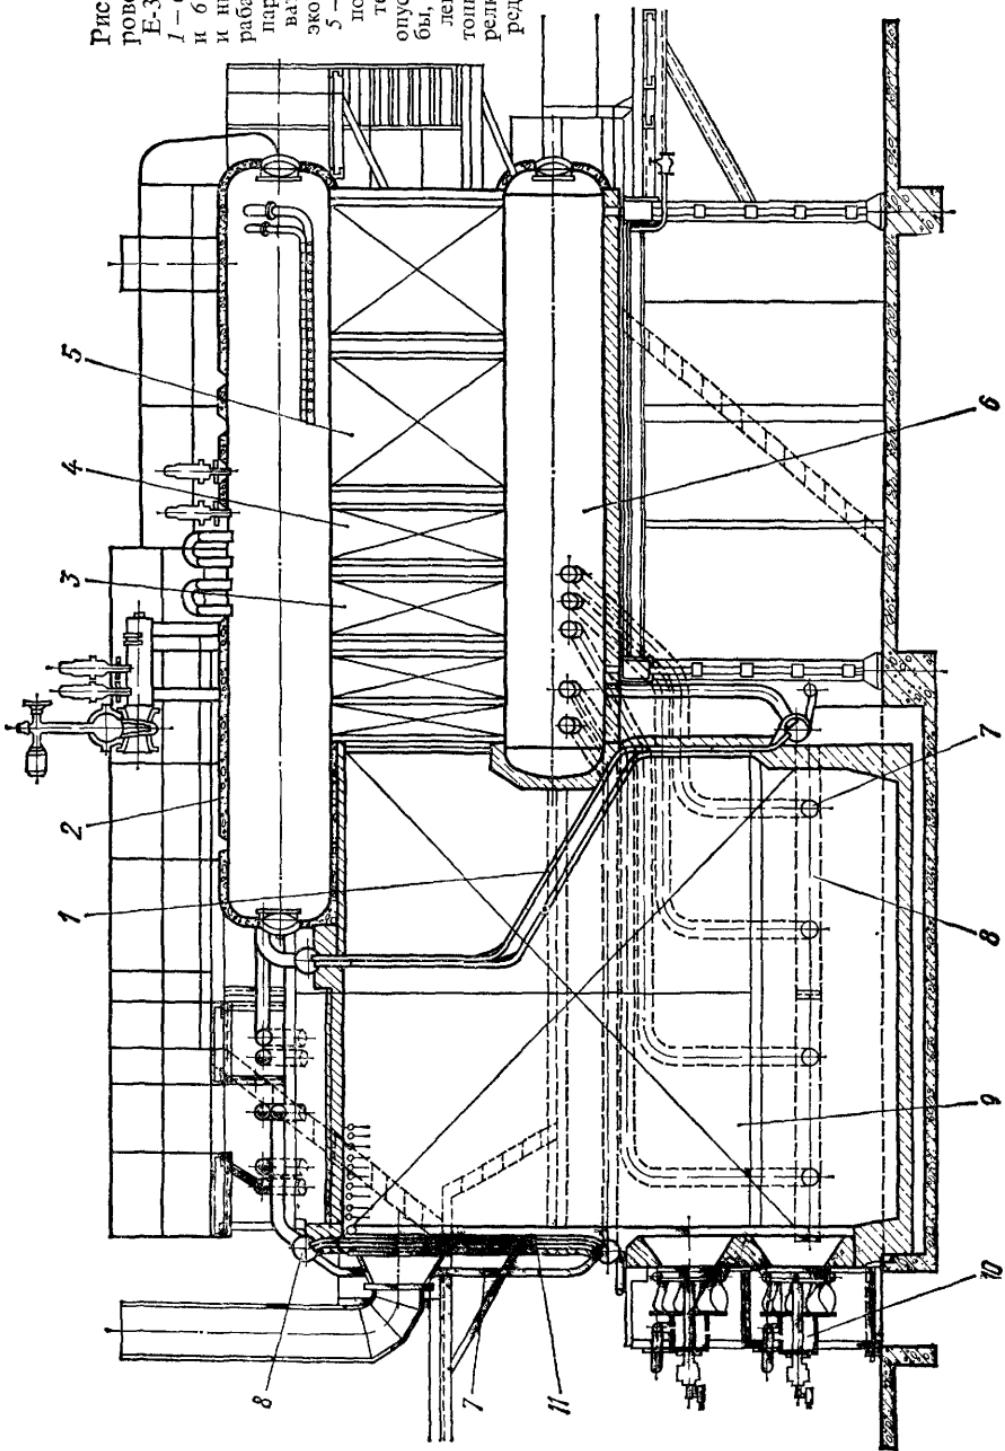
Двухбарабанный котельный агрегат ГМ-50-14 250:
